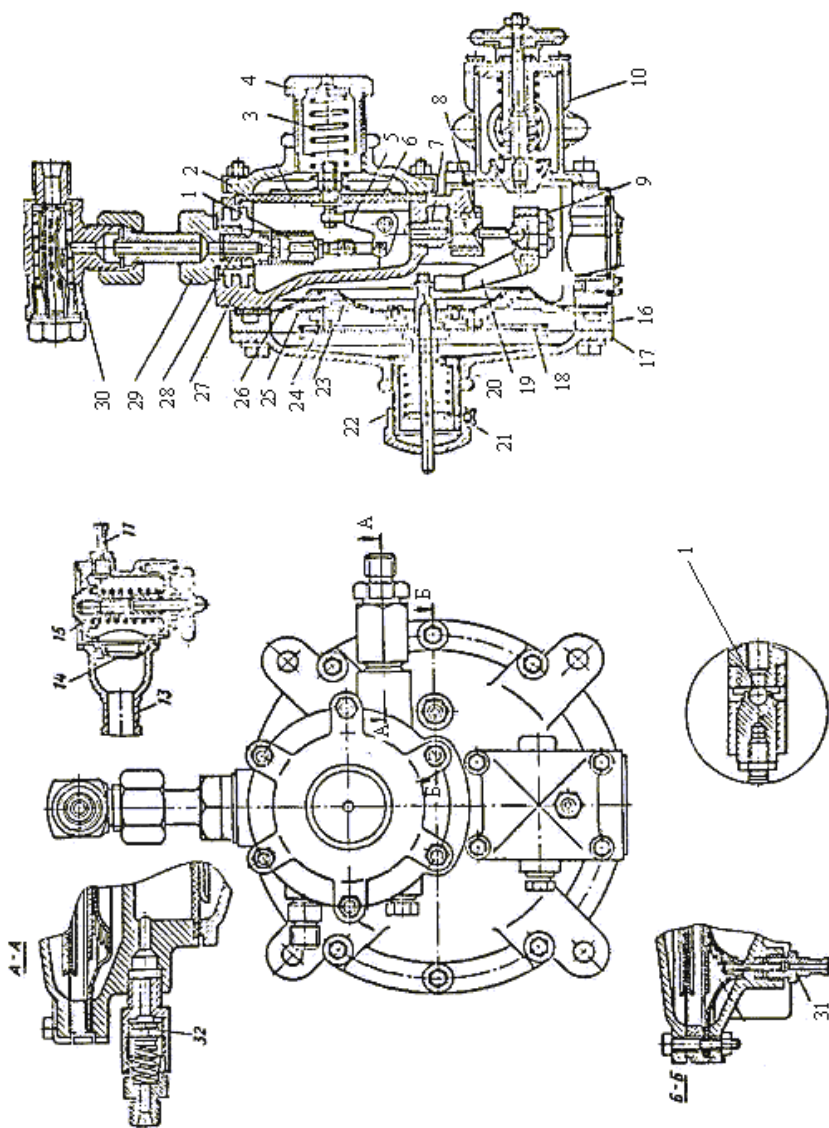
Газовий двоступінчастий редуктор МКЗ
